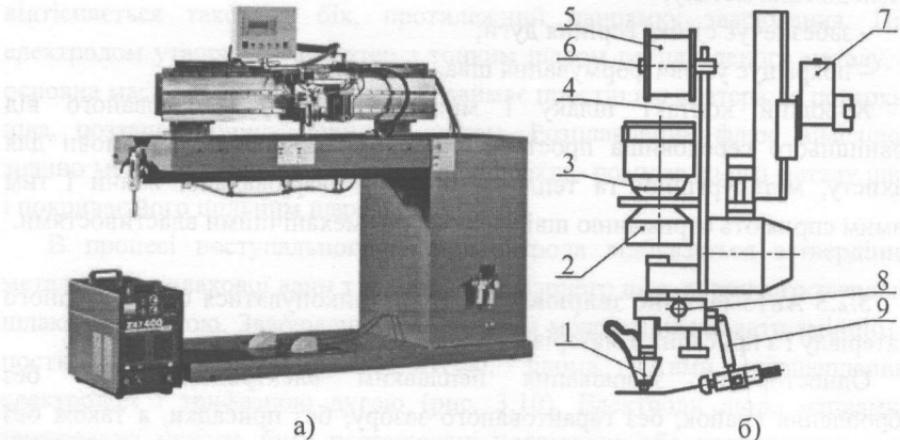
Загальний вигляд апарату для автоматичного аргонодугового зварювання з присадкою (а) і схема зварювальної головки (б): 1 – пальник, 2 – механізм подачі; 3 – привод; 4 – підвіска; 5 – касета; 6 – гальмівний пристрій; 7 – супорт; 8 – коректор; 9 – підвіска
